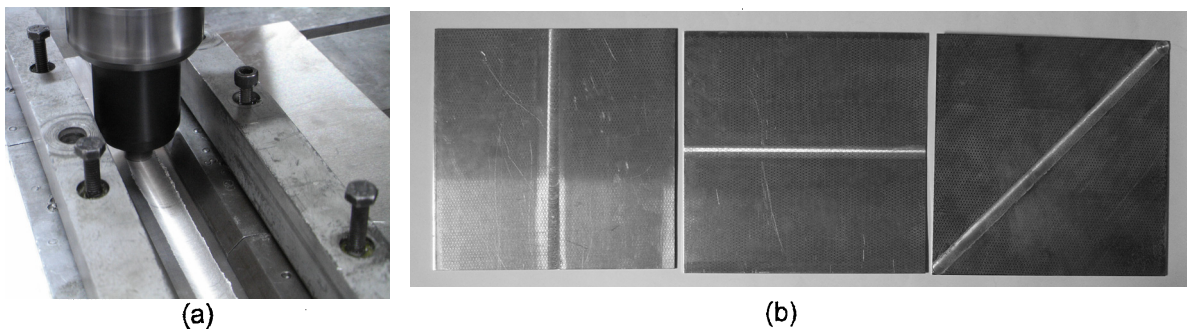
Produção de ‘tailored blanks’ de alumínio AA1050-H111 por intermédio de soldadura por fricção linear.
